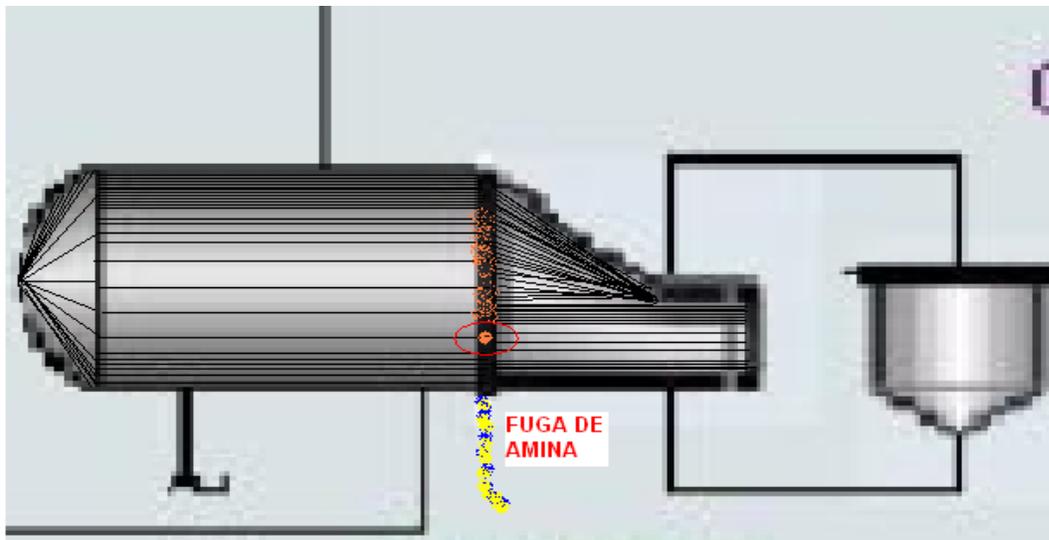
Fuga de un reboiler en cordón de soldadura
